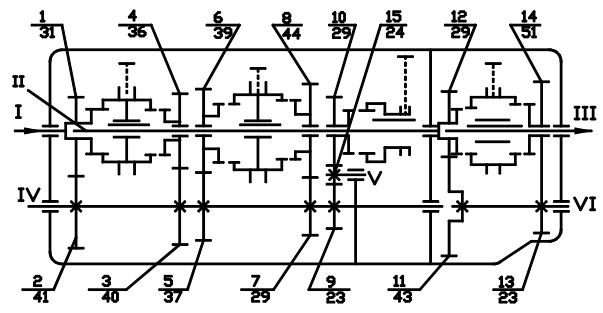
Коробка передач 8-ступенчатая с вальным редуктором
